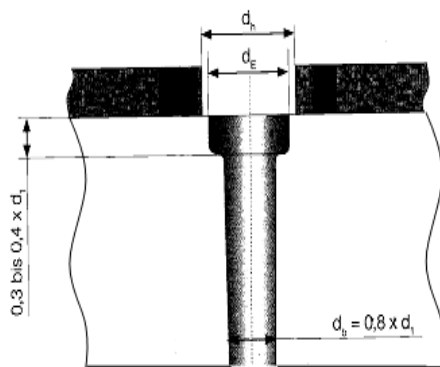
Bohrlochgestaltung für die gewindeformende Schraube
